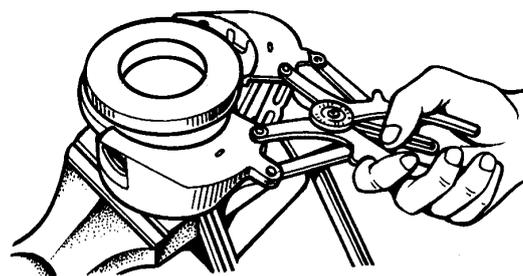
Демонтаж колец с поршня с помощью приспособления
